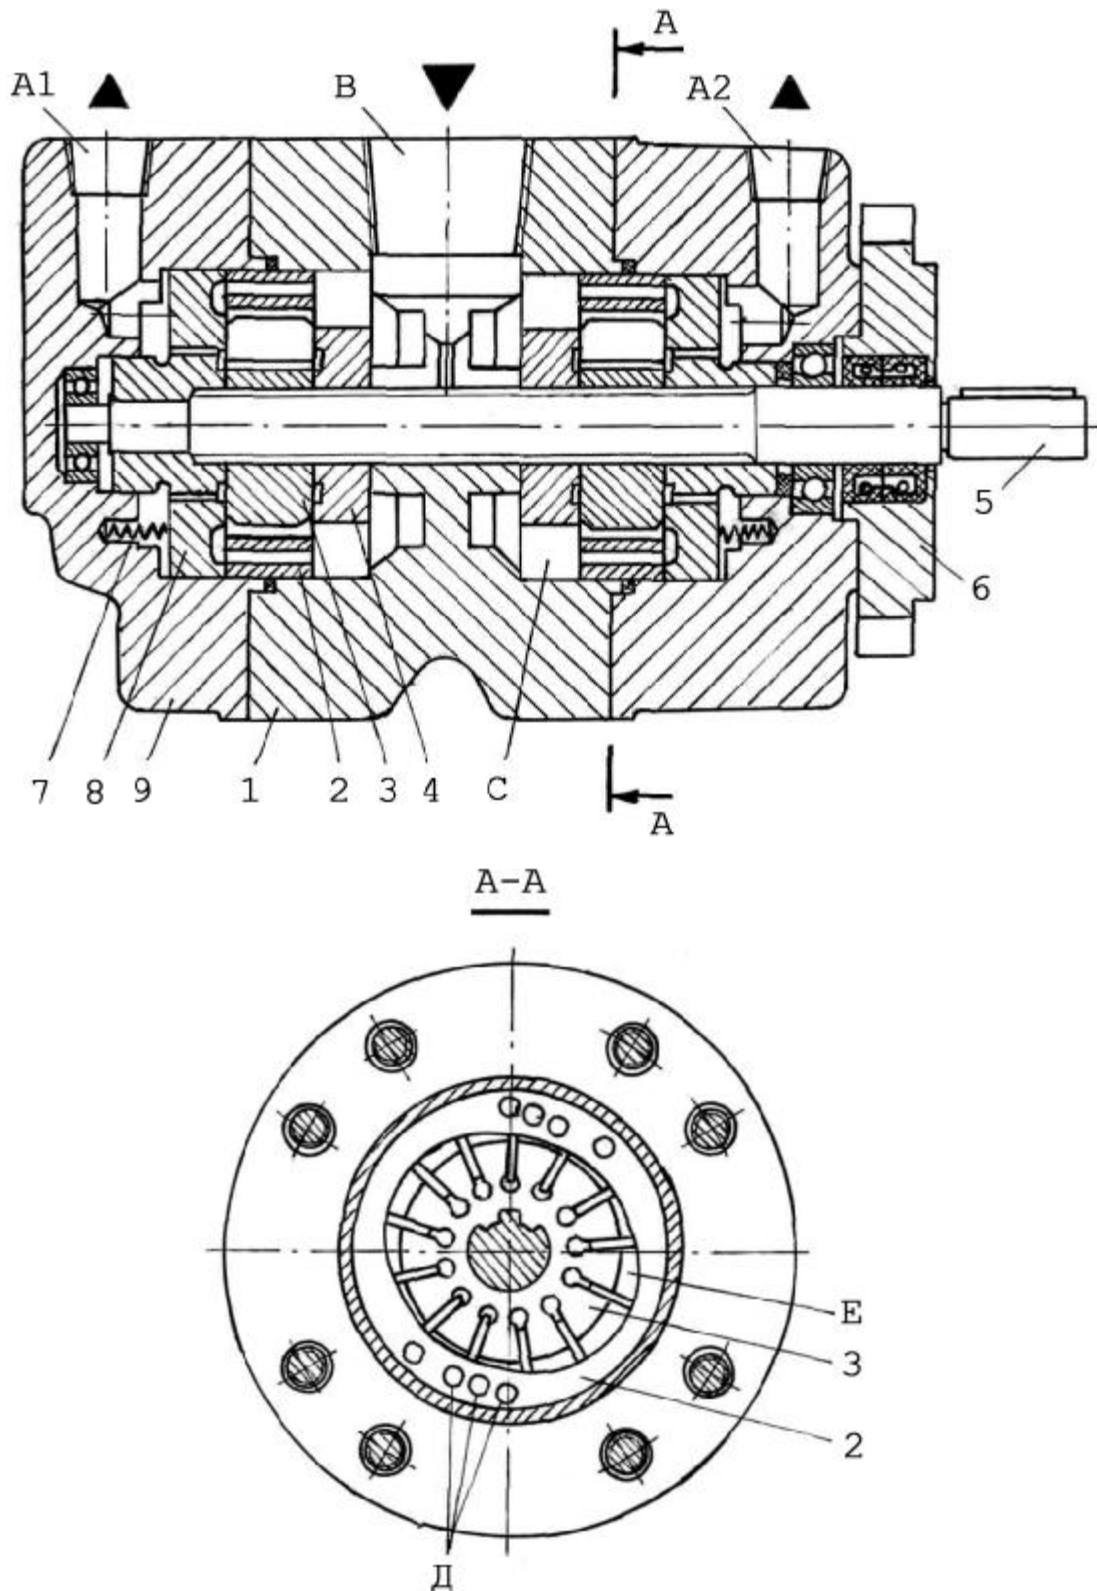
Гидронасос пластинчатый 5Г12 – 31АМ: 1 – корпус; 2 – статорное кольцо; 3 – ротор; 4 и 8 – распределительные диски; 5 – приводной вал; 6 – установочная пластина; 7 – пружина поджимная; 9 – крышка; В – линия всасывания; А1 и А2 – линии нагнетания; С – окна всасывания; Д – отверстия всасывания в статоре; Е – рабочая камера.
